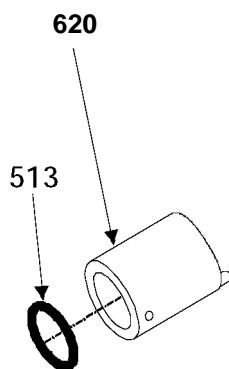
O-Ring Dichtung Demontage / Montage
